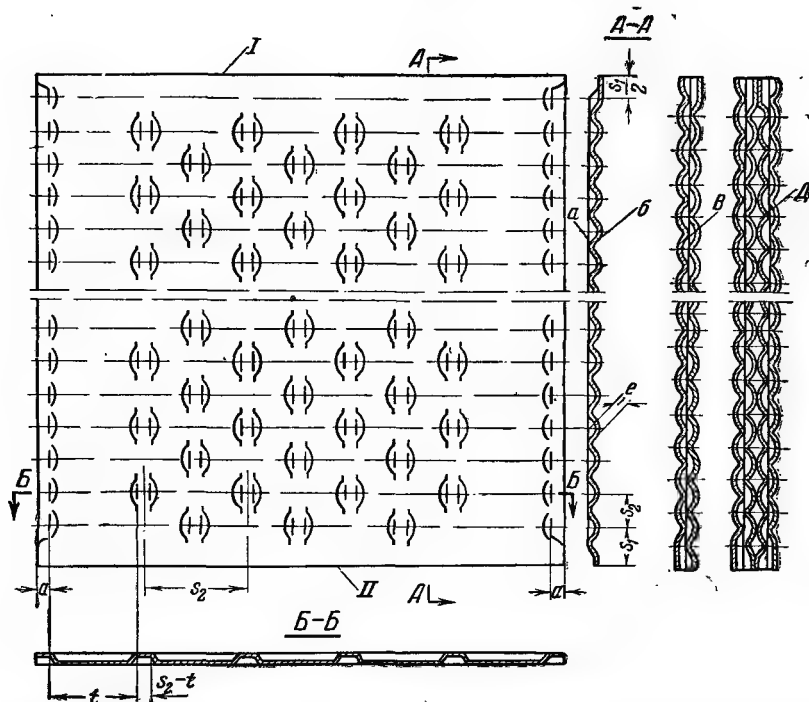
Овалообразный штампованный лист для пластинчатого теплообменника НЗЛ.
